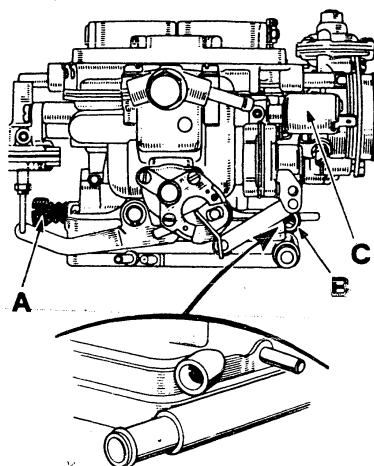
Weber-Vergaser DARA: A Einstellschraube für Leerlaufdrehzahl – B Gemischregulierschraube – C Leerlaufabschaltventil.
